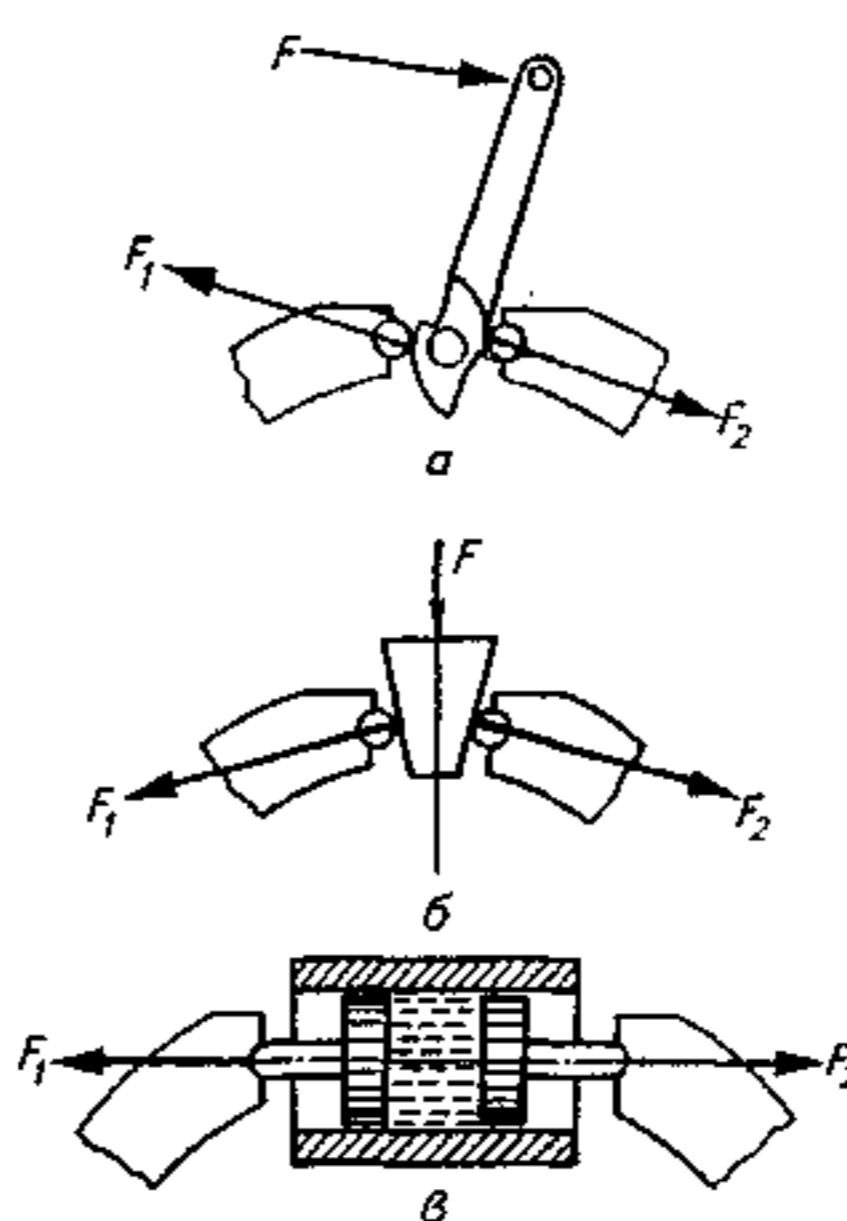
Типы разжимных устройств барабанных тормозных механизмов: а — кулак; б— клин; в — гидроцилиндр; F1 и F2 — силы, действующие на тормозные колодки.
